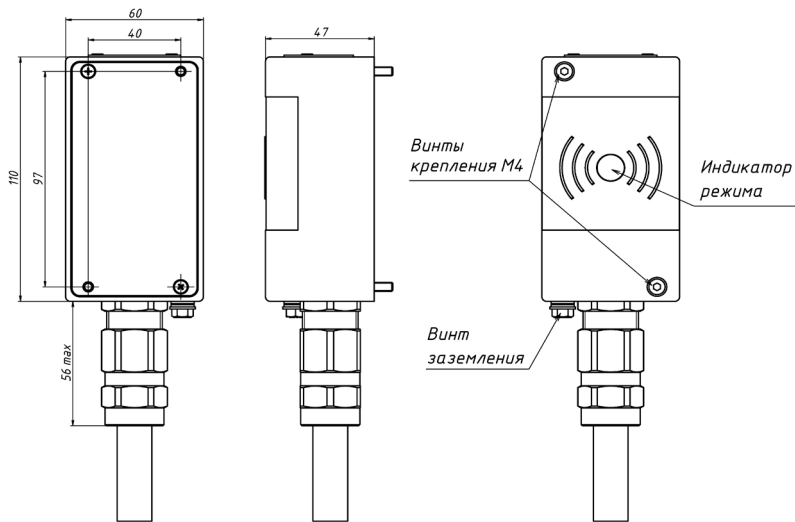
Габаритно-установочные размеры считывателя ALM-RD-S06
